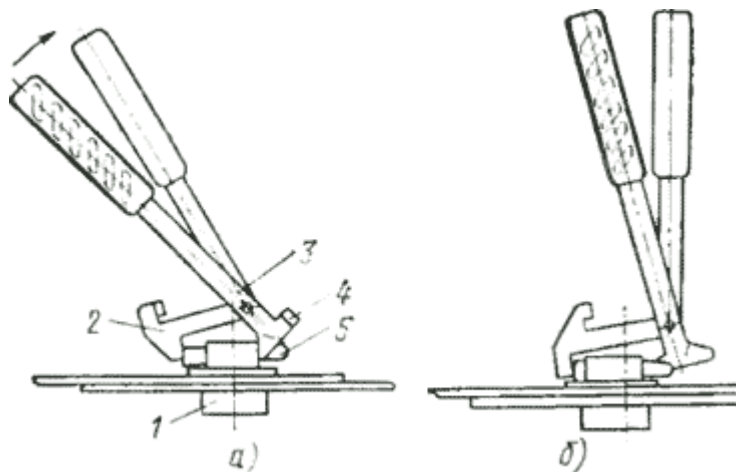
Клещи для соединения УСЭЖ клиновыми соединителями
